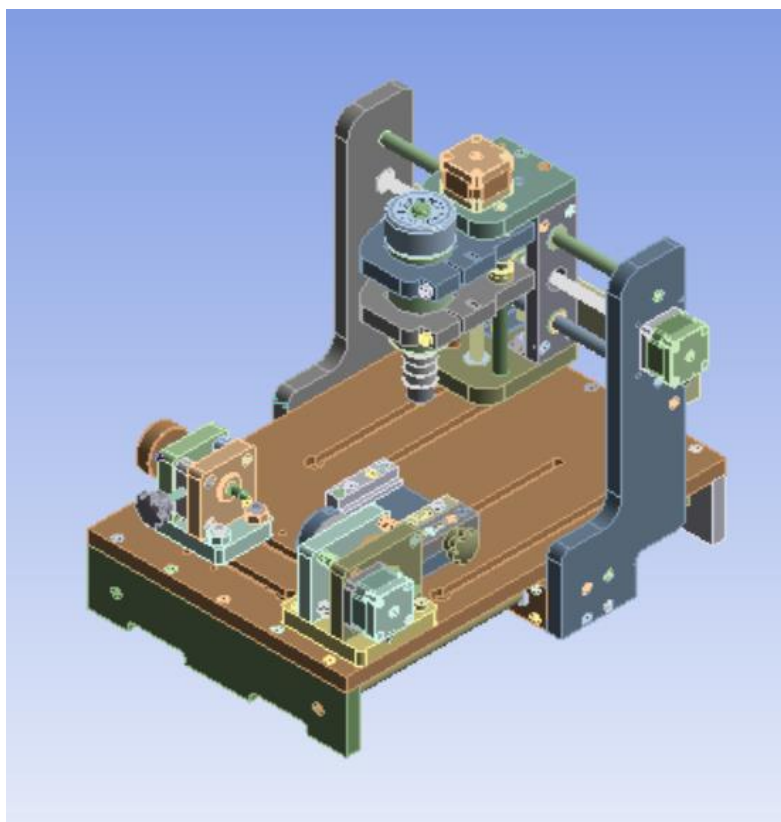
CAD модель вертикально-фрезерного верстата в середовищі ANSYS
